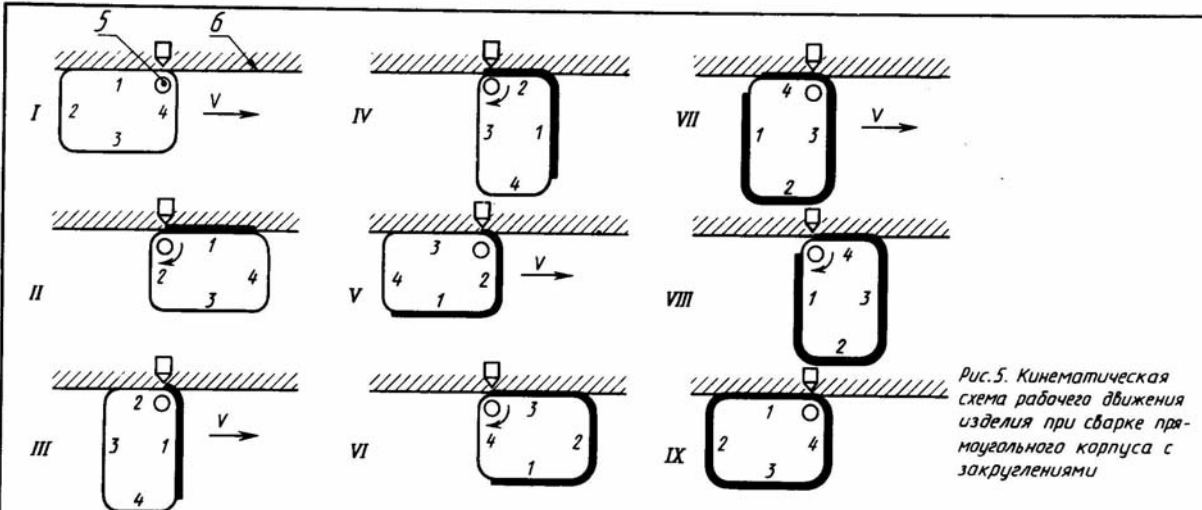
Кинематическая схема рабочего движения изделия при сварке прямоугольного корпуса с закреплениями
